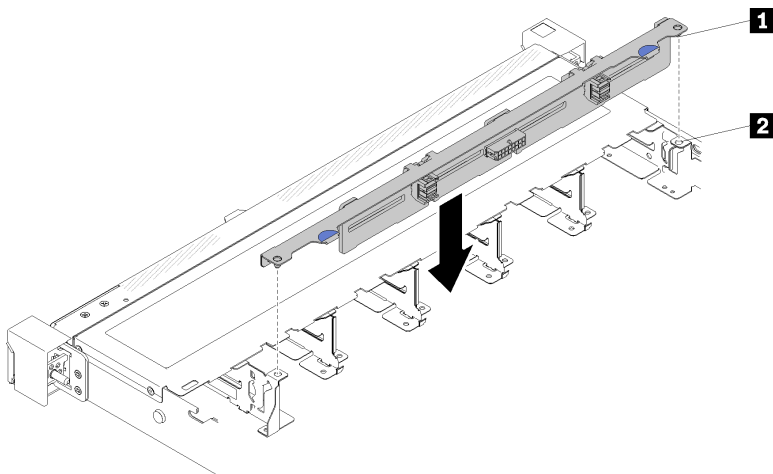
Installation d'un fond de panier d'unité 3,5 pouces remplaçable à chaud
